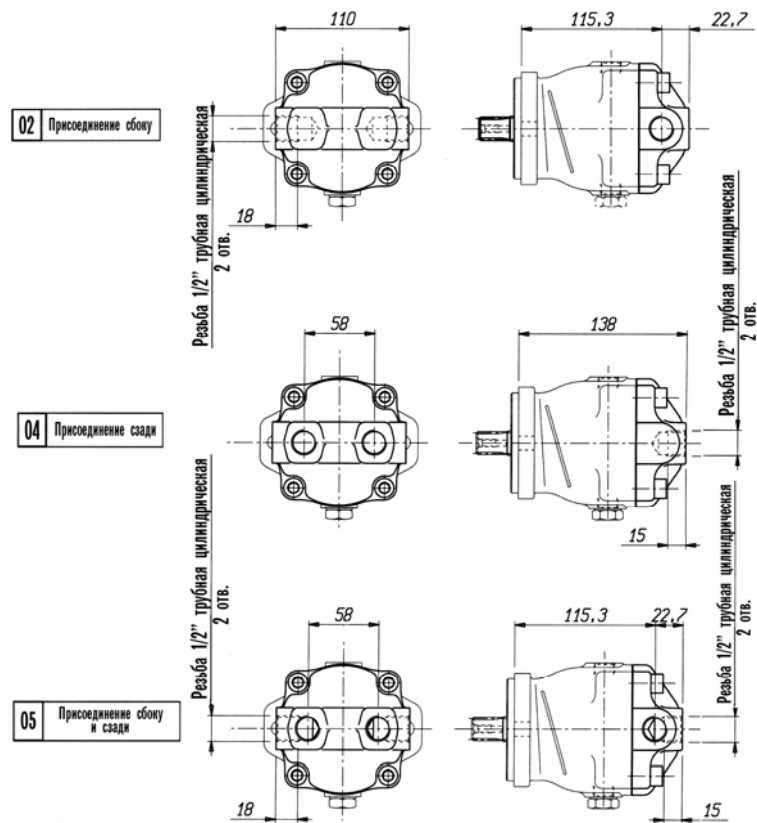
Присоединительные отверстия в корпусах гидромоторов
